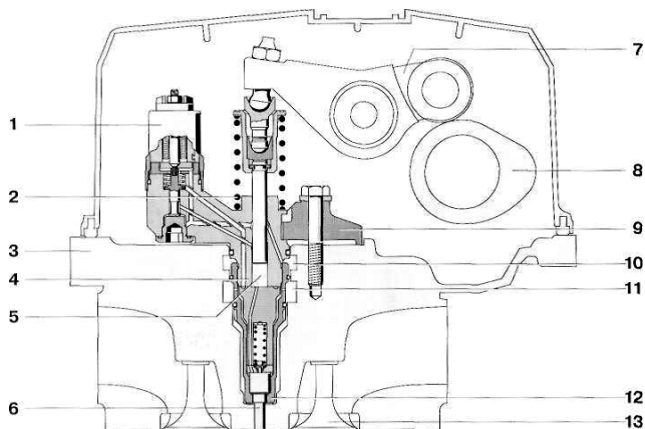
Установка насос-форсунки в головке блока цилиндров двигателя:
